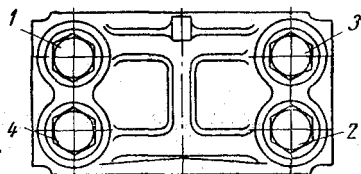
Порядок затягивания болтов крепления средней и задней крышек коренных подшипников
